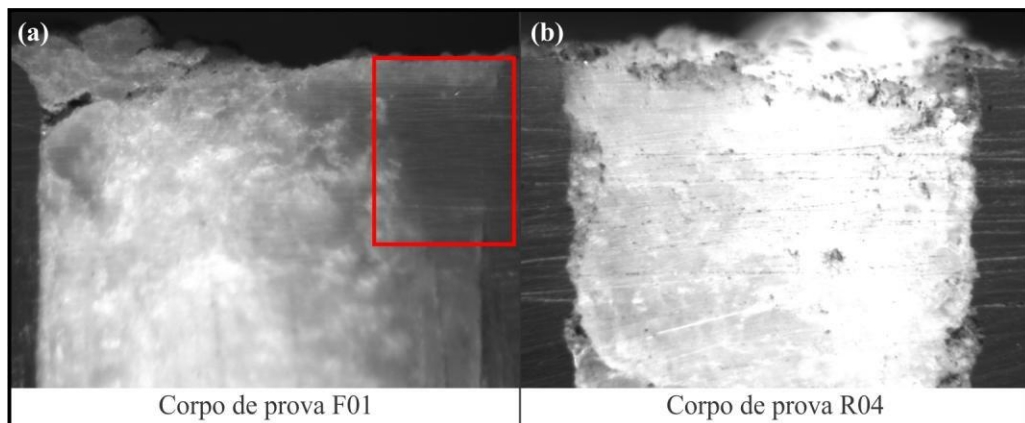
Ausência de cordão de solda durante soldagem com ferramenta com geometria de pino roscado. a) Eliminação total do cordão de solda. b) Eliminação parcial do cordão de
